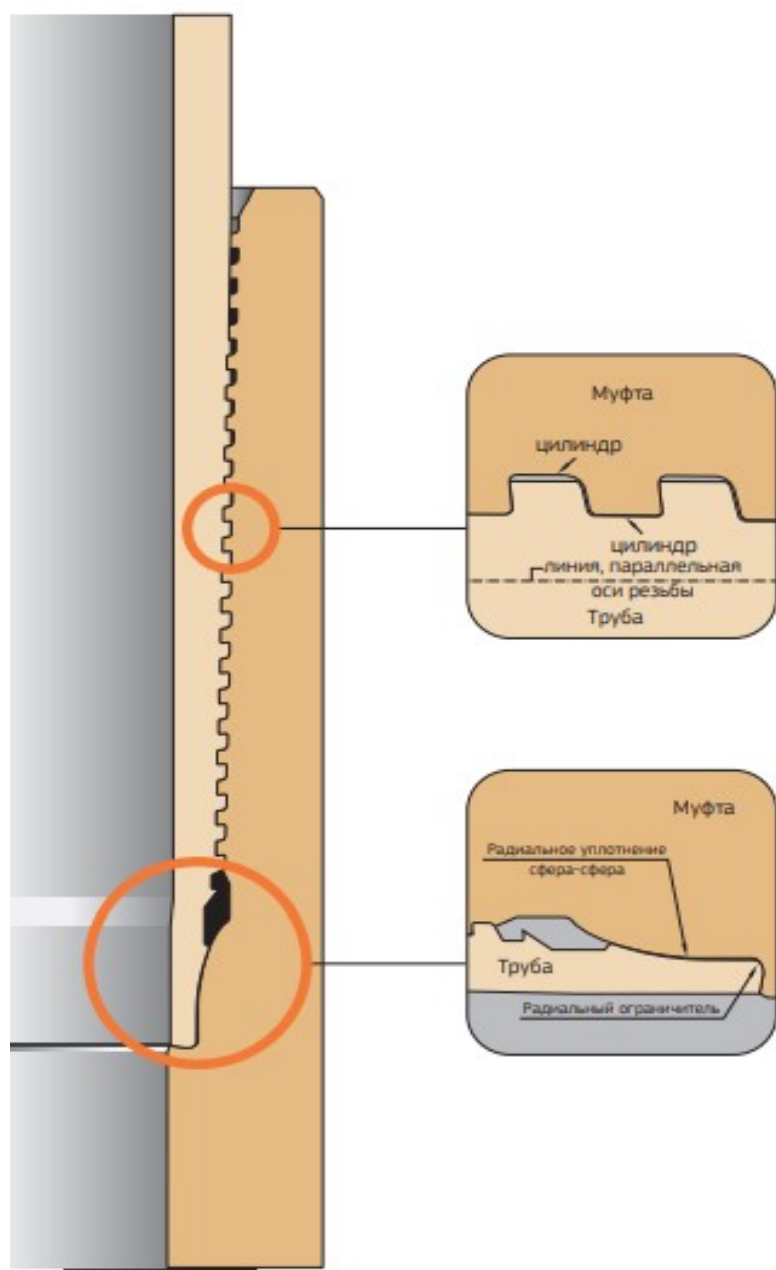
Резьбовое соединение «ТМК UP CENTUM»
